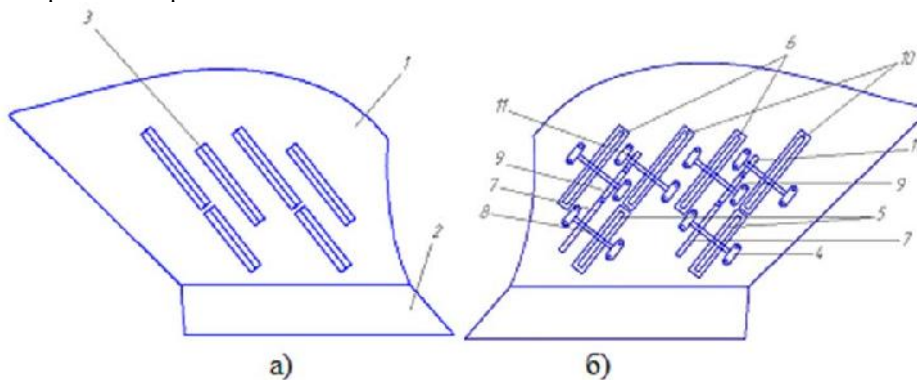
Корпус плуга вид спереди а) и вид сзади б)
